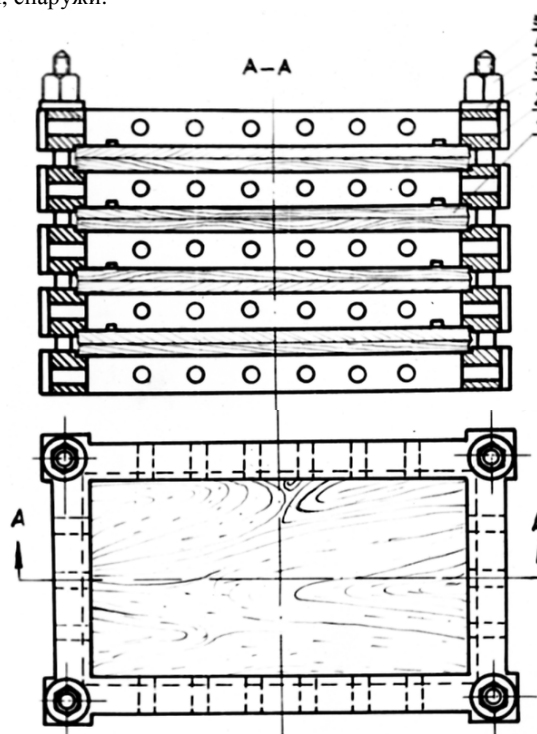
Приспособление для импрегнирования древесного шпона разнородными материалами: 1 – шпон; 2 – зажимы; 3 – стержень; 4 – гайка.
